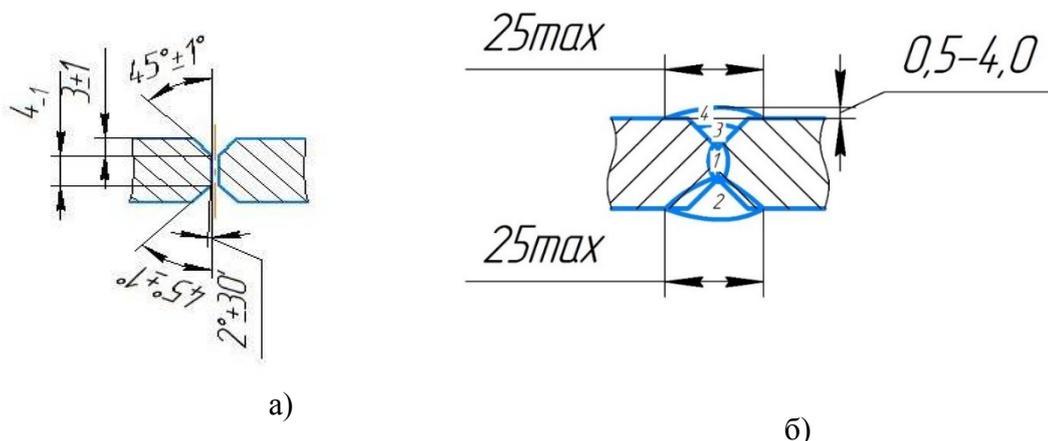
Схемы разделки кромок и наложения сварных швов: а) эскиз разделки пластин; б) схема наложения валиков при односторонней многопроходной автоматической сварке
